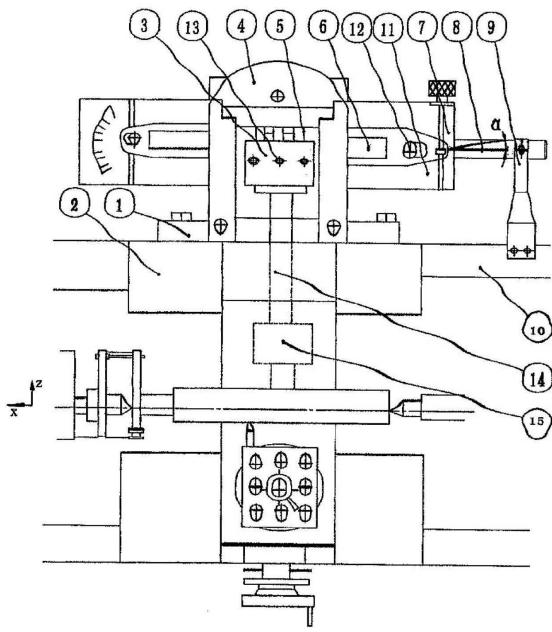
Конструкция приспособления для токарной обработки конуса
